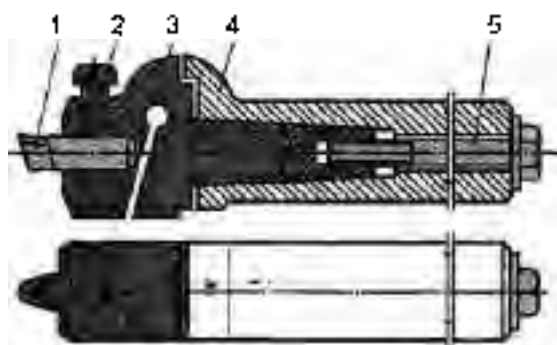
ДЕРЖАВКА З ПОВОРОТНОЮ ГОЛОВКОЮ ДЛЯ НАРІЗНОГО РІЗЦЯ:
